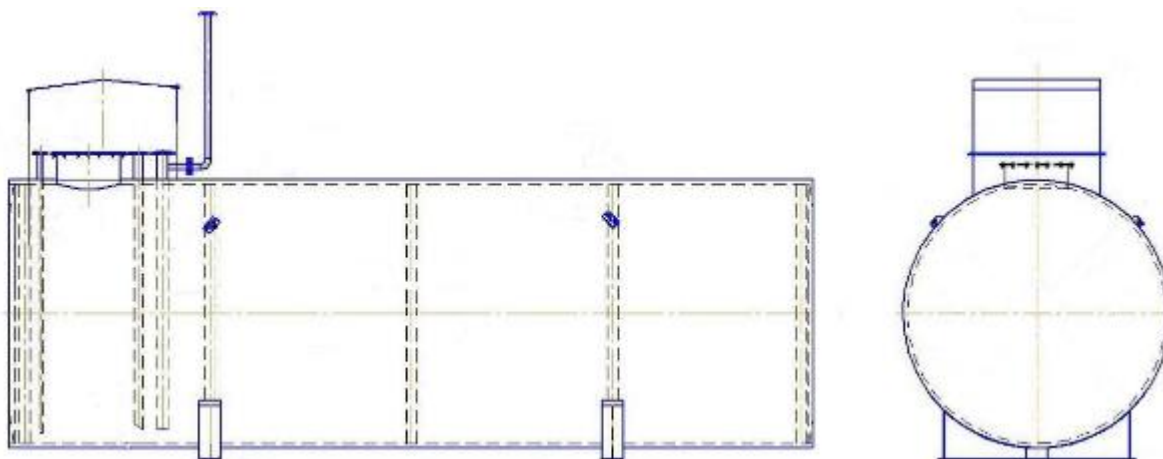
Эскиз общего вида резервуаров РГС-20 зав.№ 1, РГС-50 зав.№ 2
